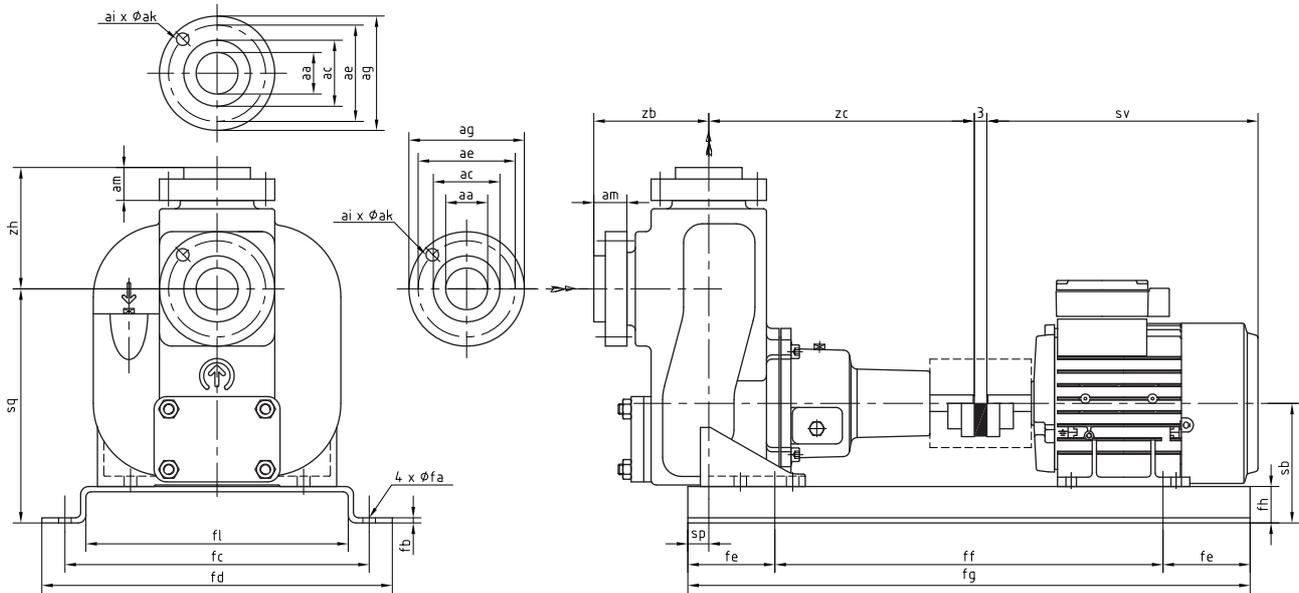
FRE - Pumpenaggregat A6, mit ISO 7005 PN20 Anschlüssen.
